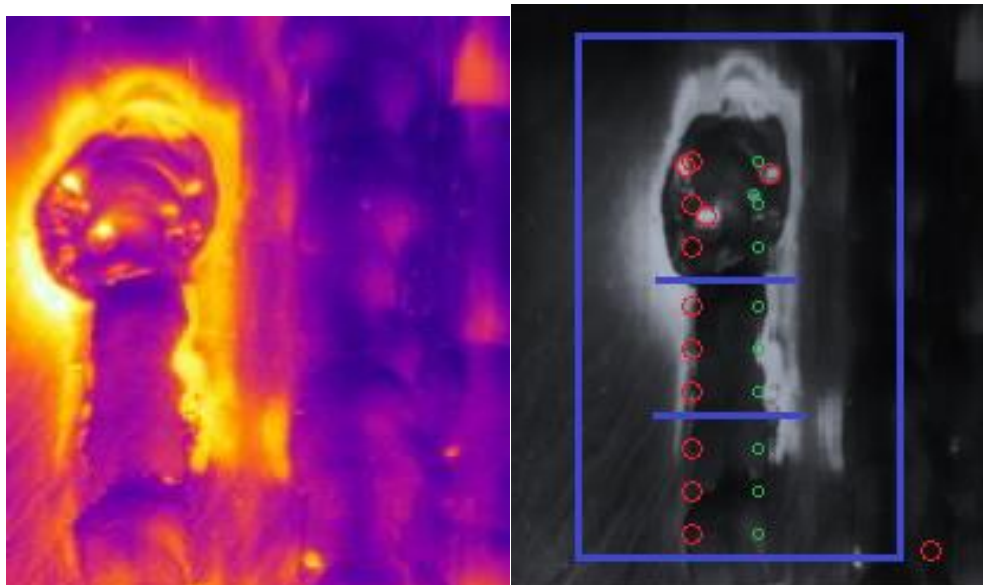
Cordón de soldadura afectado por porosidad (1).
